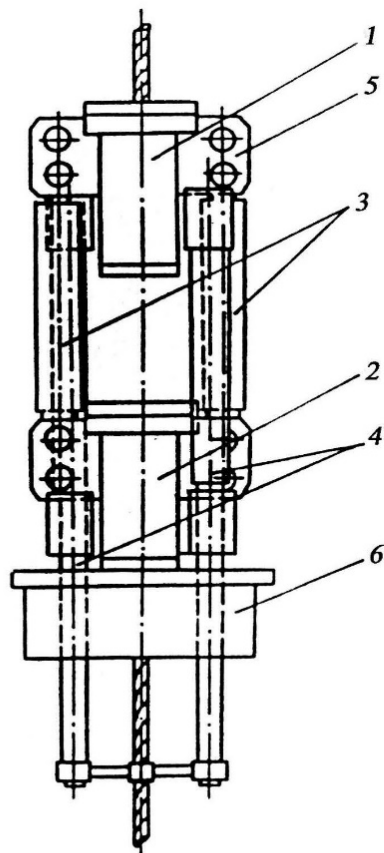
Гідралічний підйомник розроблений КНУ
